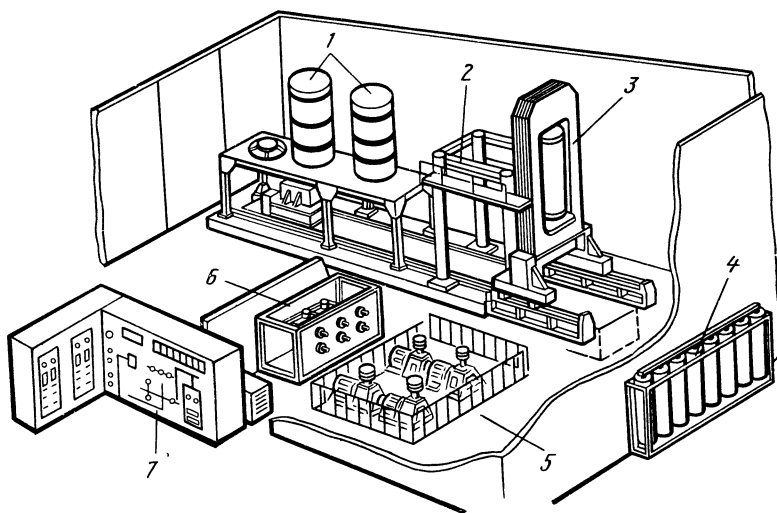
ГПМ для прессования заготовок из металлического порошка:
